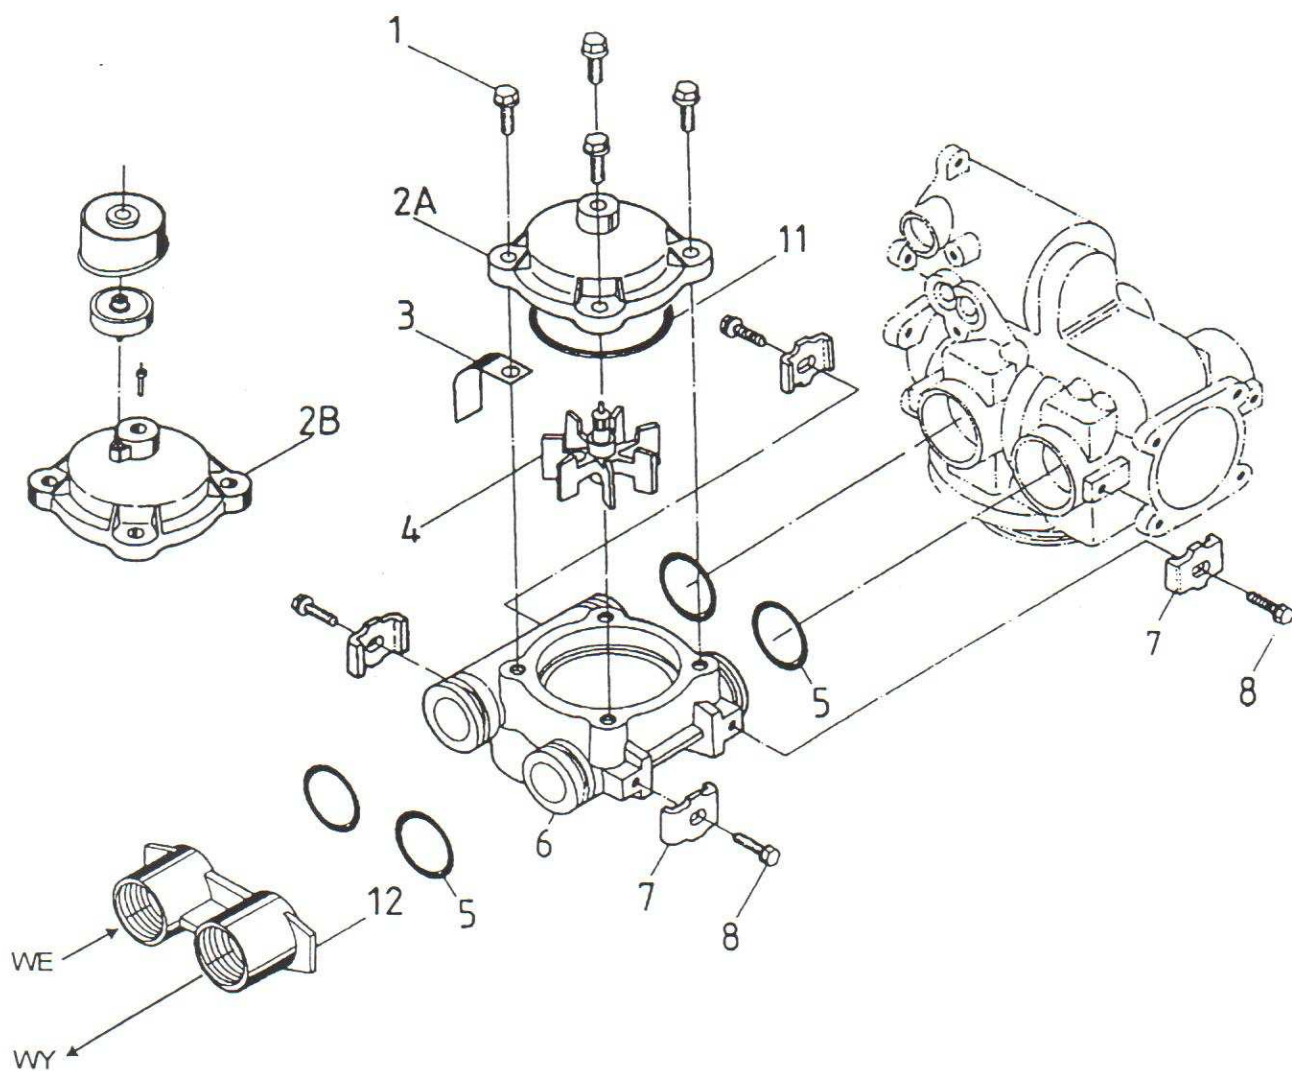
/56/90/95/916 Budowa zaworu solankowego dla zmiękczacza 27, 56, 90 i 95.
